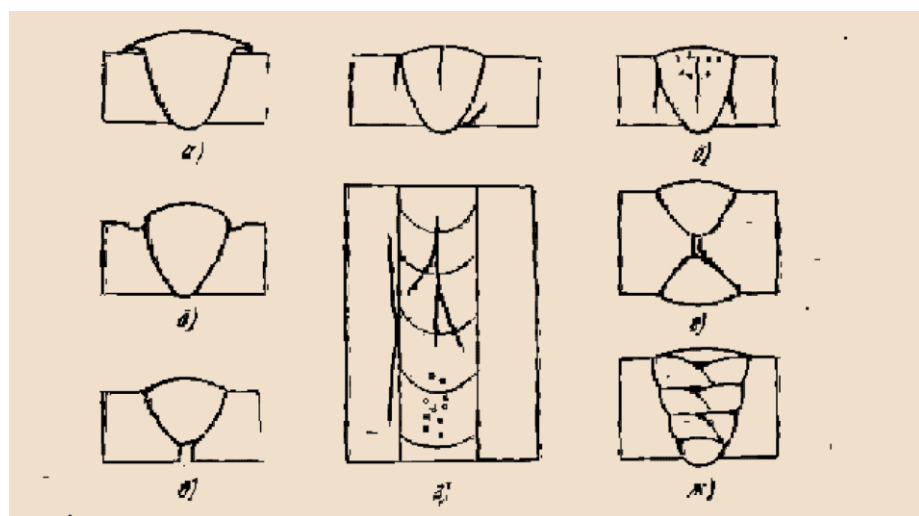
Виды дефектов в сварных соединениях:
